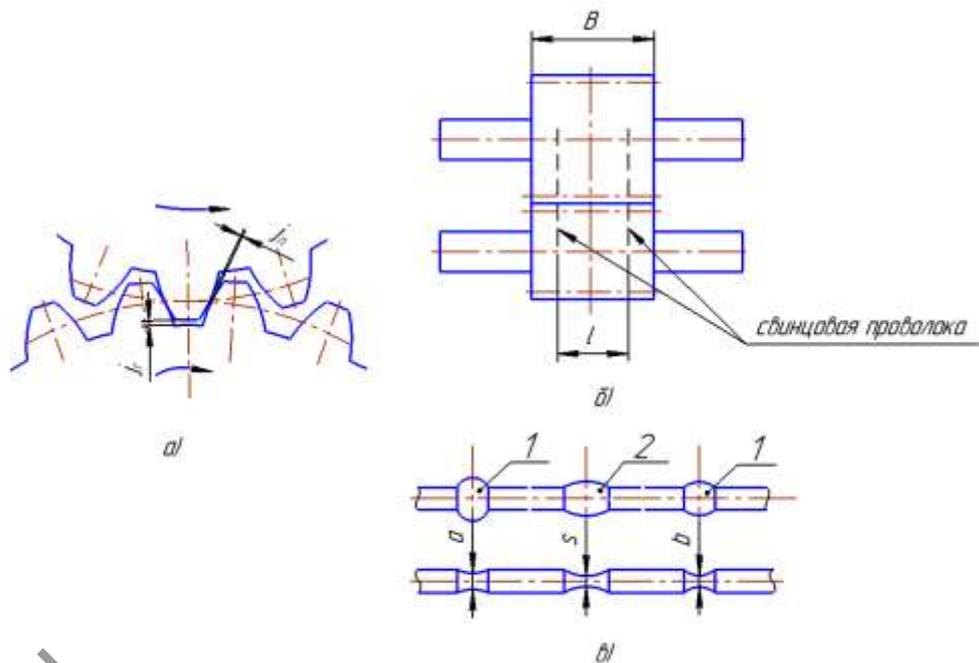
Схемы образования и проверки бокового и радиального зазоров: а) образование зазоров; б) схема наложения проволоки на зубья; в) форма оттисков
